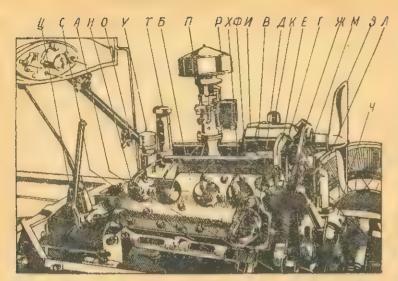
Общий вид 8-цилиндрового двигателя Форд (спере-
